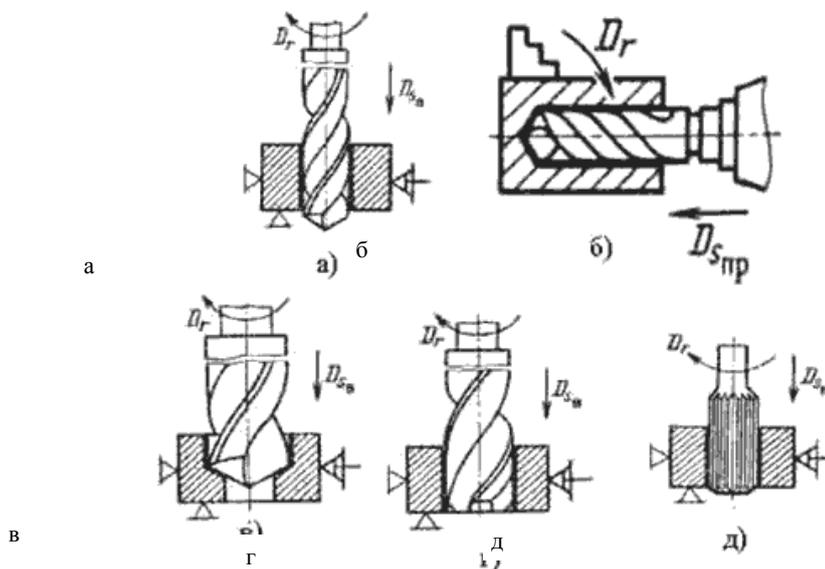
Схемы обработки металлов резанием: а – в – сверление, г – зенкерование, д – развертывание
